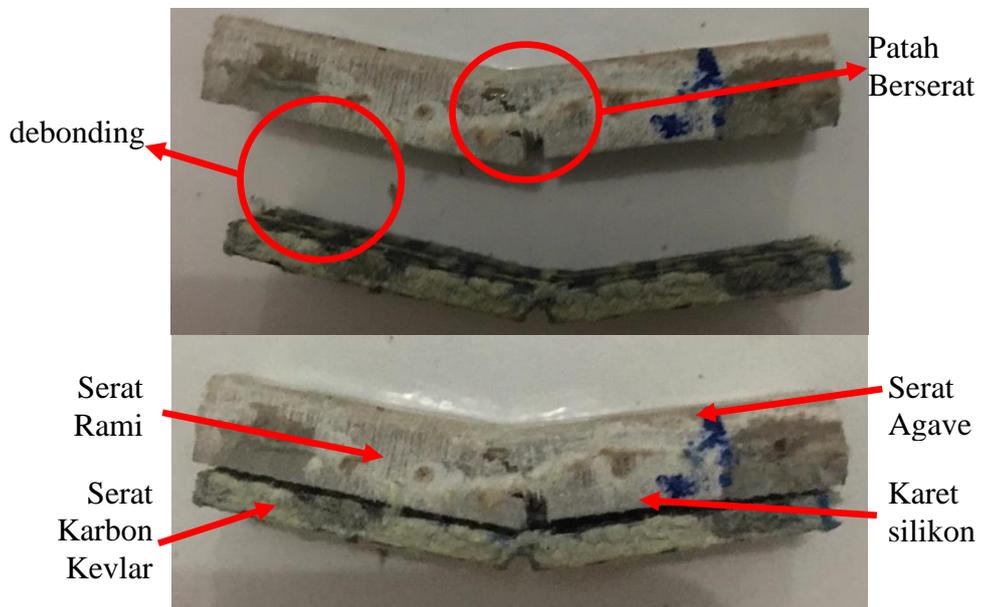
8 Foto patahan salah satu specimen 30% karet silikon
